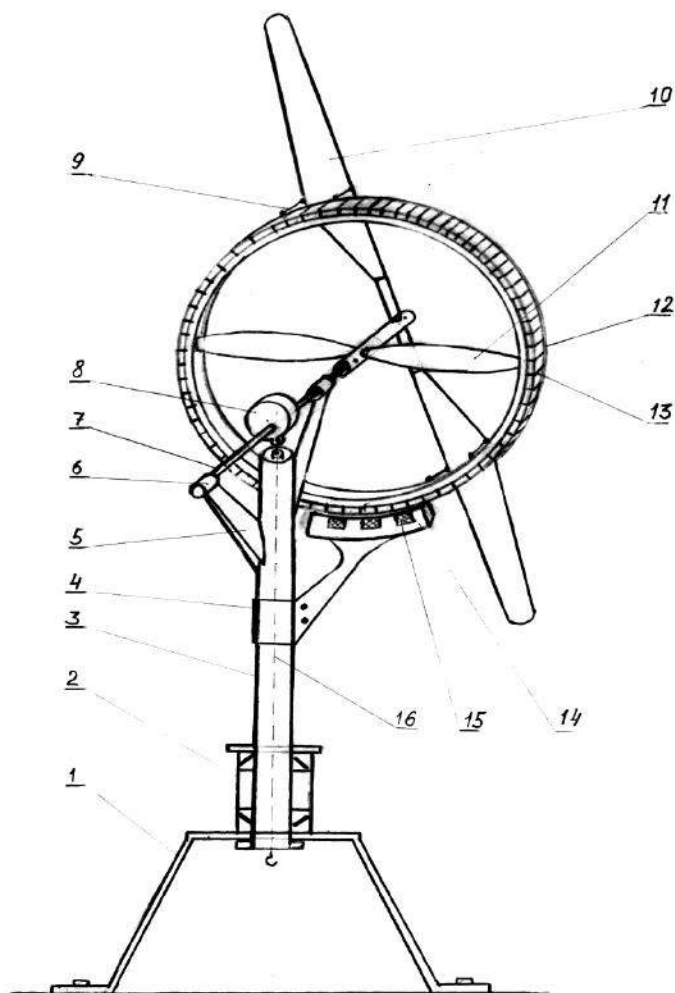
Загальна конструктивна схема безредукторної вітроенергетичної установки: 1 – рама основи; 2- підшипниковий вузол; 3 – поворотна стійка; 4 – штатив статора; 5- кронштейн кріплення вала; 6 – підшипниковий вузол; 7 – вал ротора; 8- ексцентрик; 9 – з’єднувальні тяги; 10- основні лопаті;11 – допоміжні лопаті;12 – кільцеподібний ротор; 13 – активні елементи ротора; 14 – дугоподібний статор; 15- обмотки статора; 16 –тяга механічного приводу
